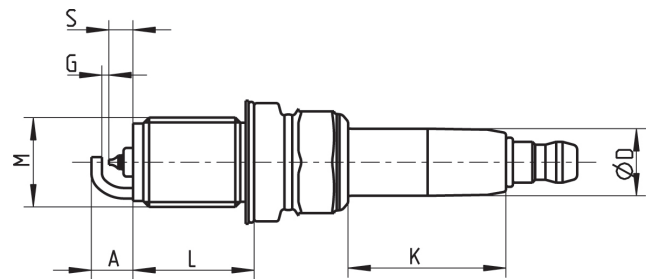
Dimensionen der Zündkerze Typ 6115B...
